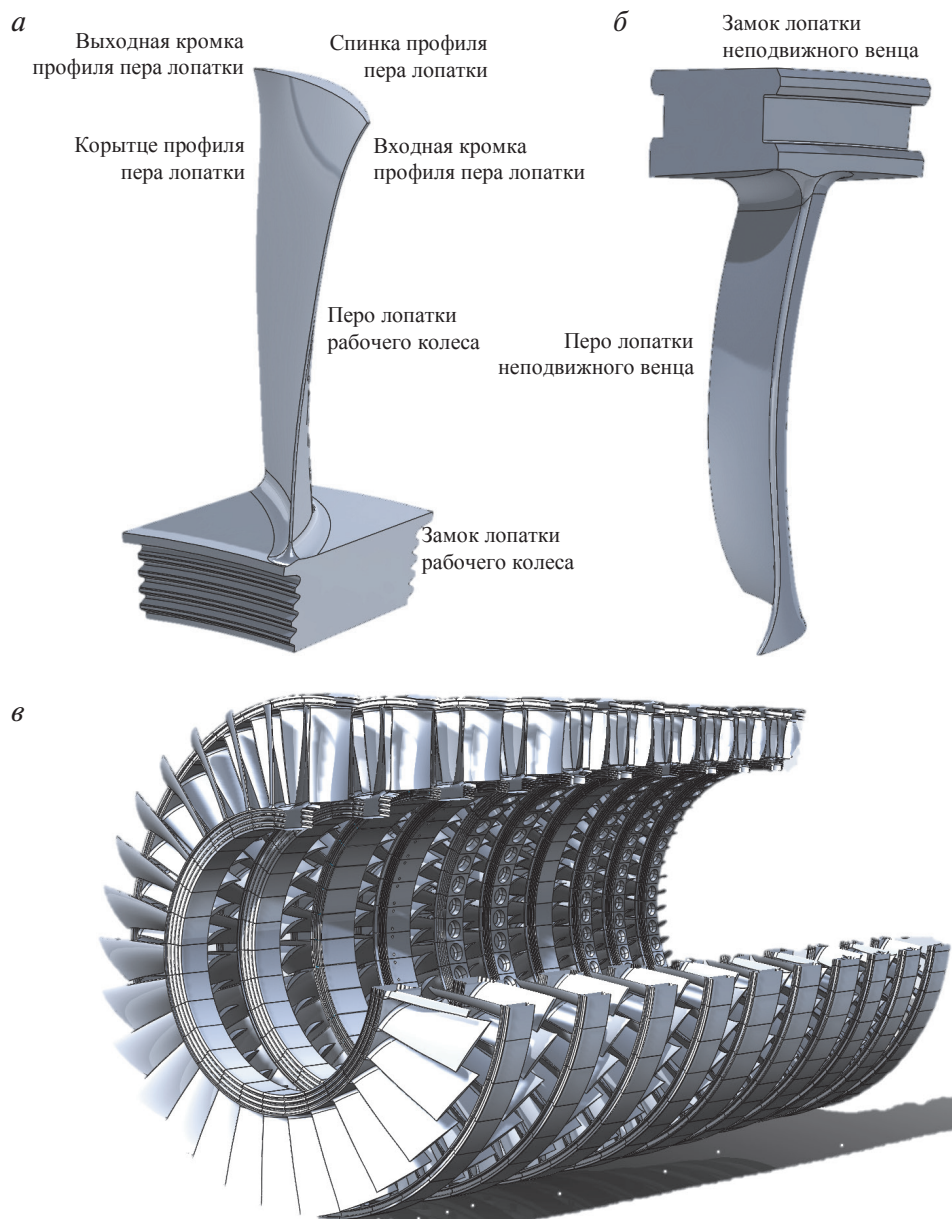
Лопаточный аппарат осевого компрессора:
